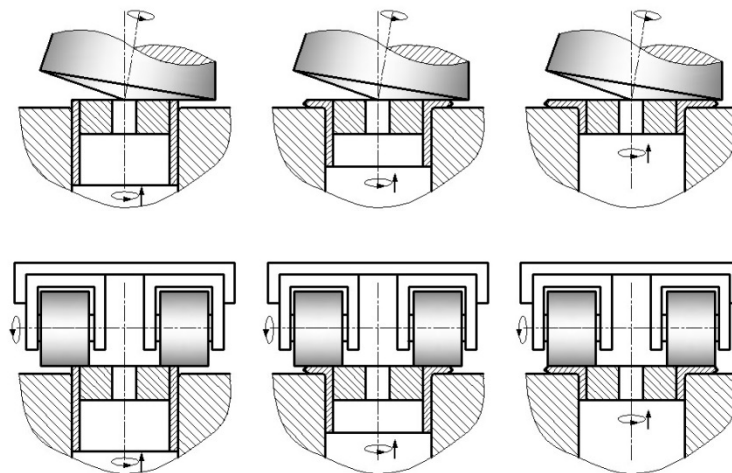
Схема раскатки с выдавливанием утолщенных фланцев коническим и цилиндрическими валками
